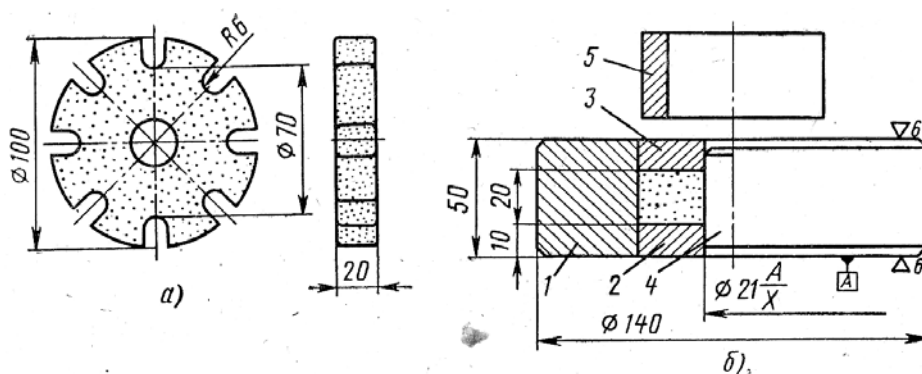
Прессованный круг на бакелитовой связке (а) и пресс-форма для его изготовления (б).
